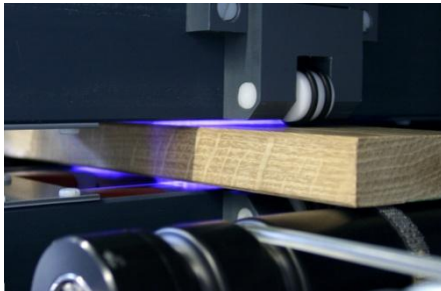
Plasmabeschichtung einer Holzoberfläche
